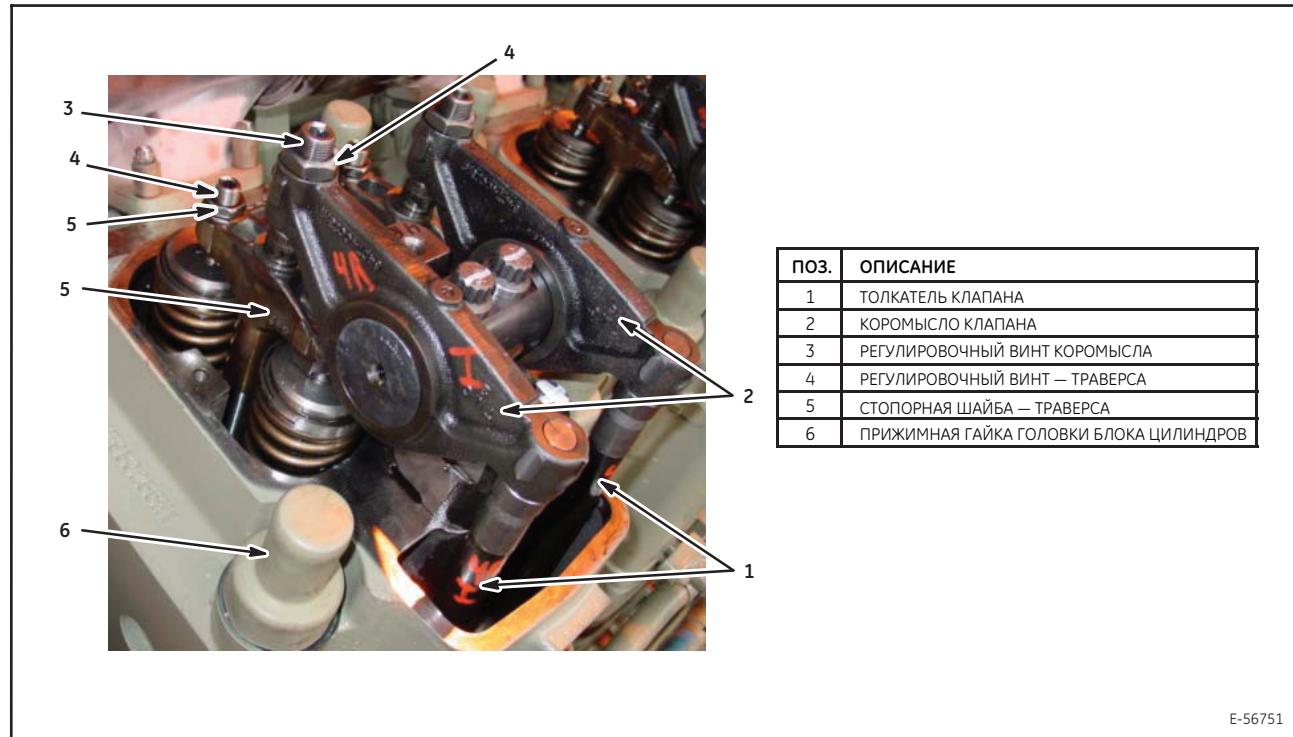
Штифтовая траверса клапана — головка цилиндров без форсунки инжектора
